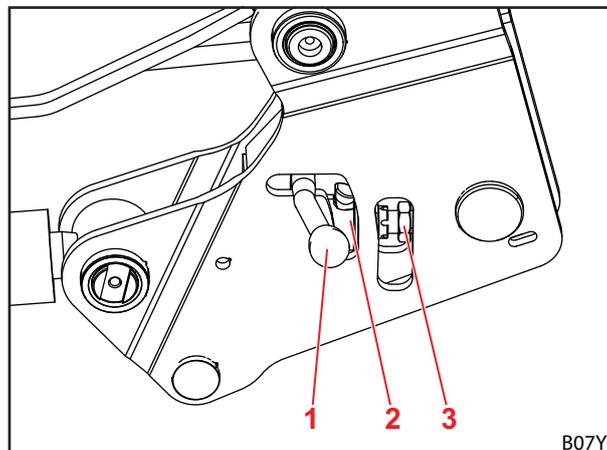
Apertura del dispositivo di blocco del caricatore frontale
